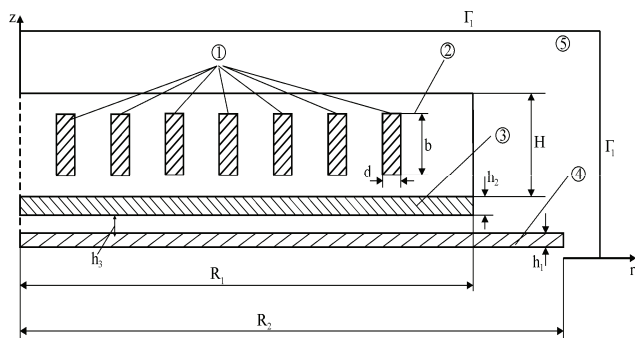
Розрахункова схема складеного багатовиткового індуктора із допоміжним екраном та заготовки: 1 – багатовитковий струмопровід; 2 – допоміжний екран; 3 – діелектричний бандаж; 4 – заготовка; 5 – оточуюче середовище (повітря)
